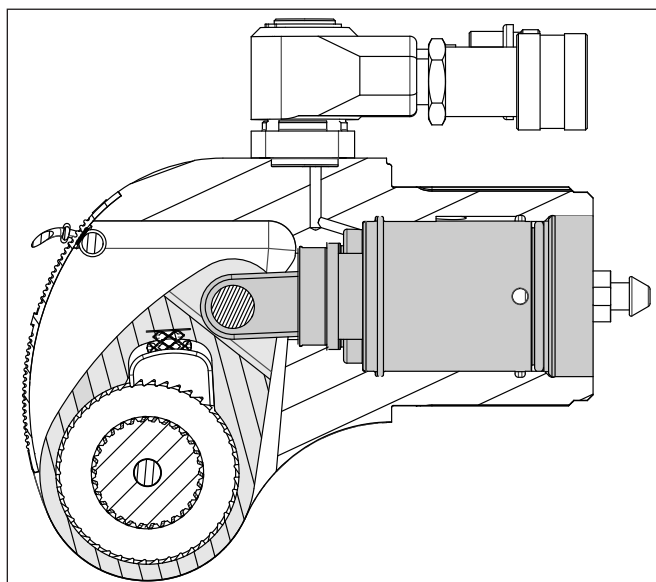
Vista in sezione del pistone di posizionamento e della leva di azionamento
